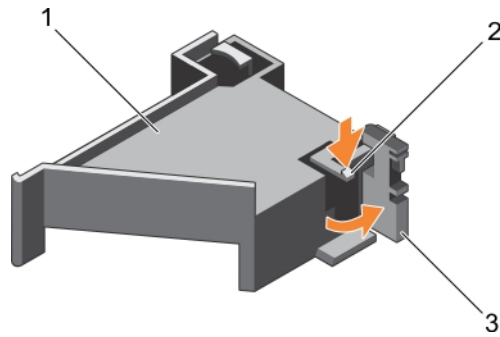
Ouverture et fermeture du loquet du support de carte PCIe
